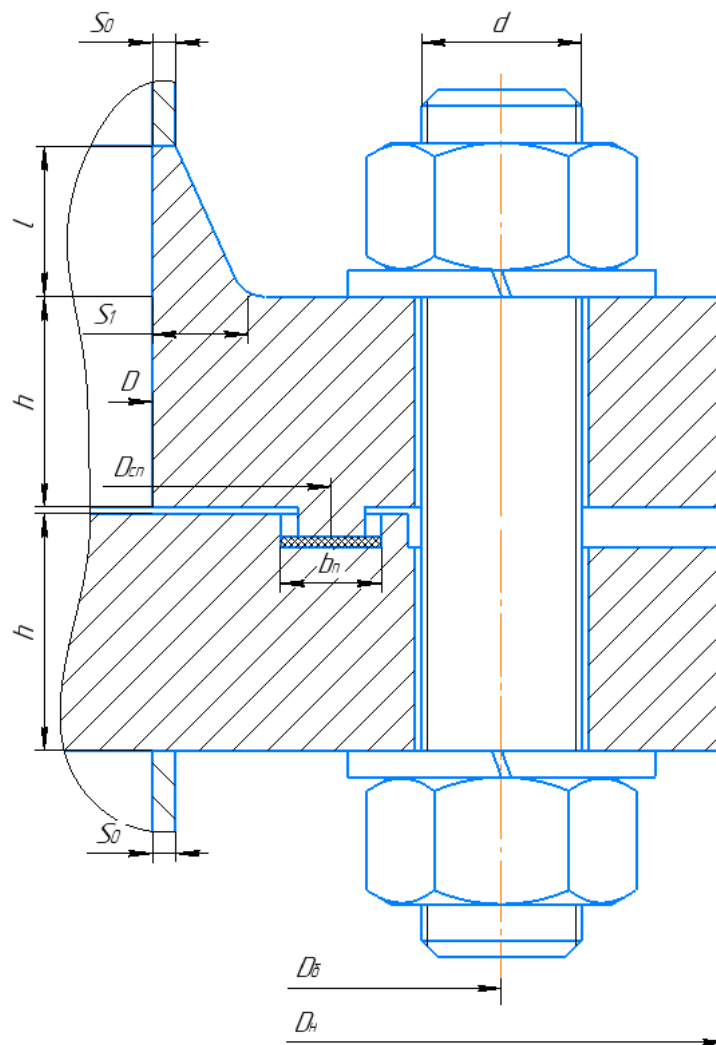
Фланцевое соединение с приварными встык фланцами с уплотнительной поверхностью типа шип-паз [22]
